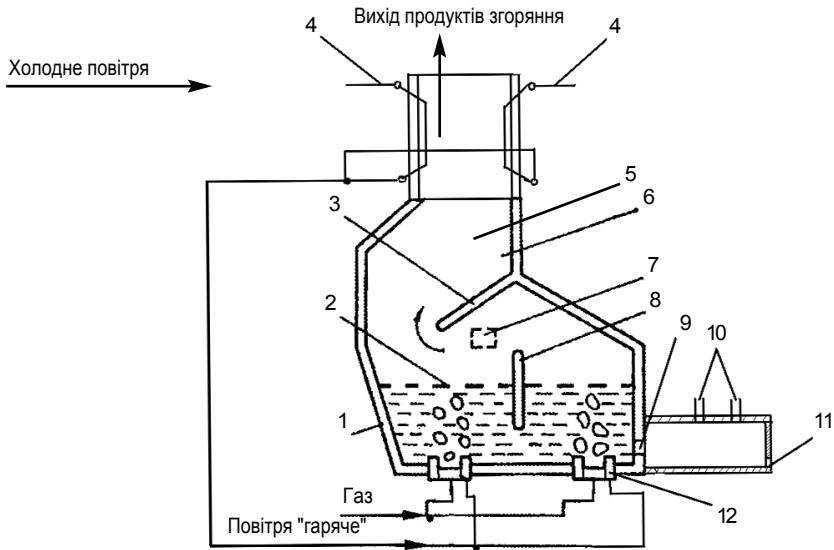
Схема безкоксового плавильного агрегату конвертерного типу:
